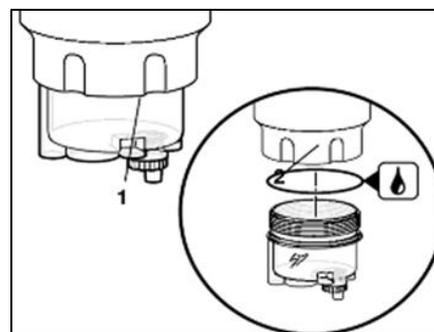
Е Установка колбы фильтра грубой очистки топлива
